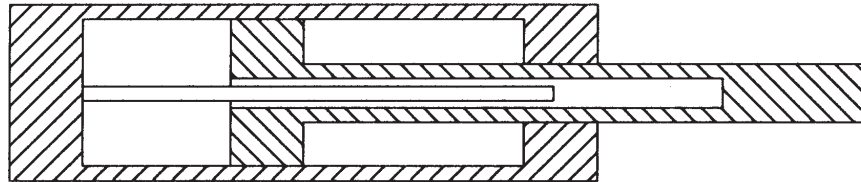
Hydraulikzylinder mit eingebautem Wegmesssystem
